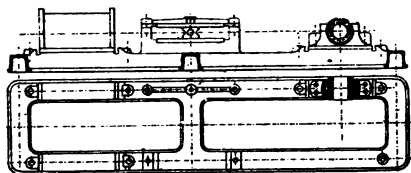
43. Rahmen mit Rundführung für Maschinen von 300—2000 Kolbenhub.
